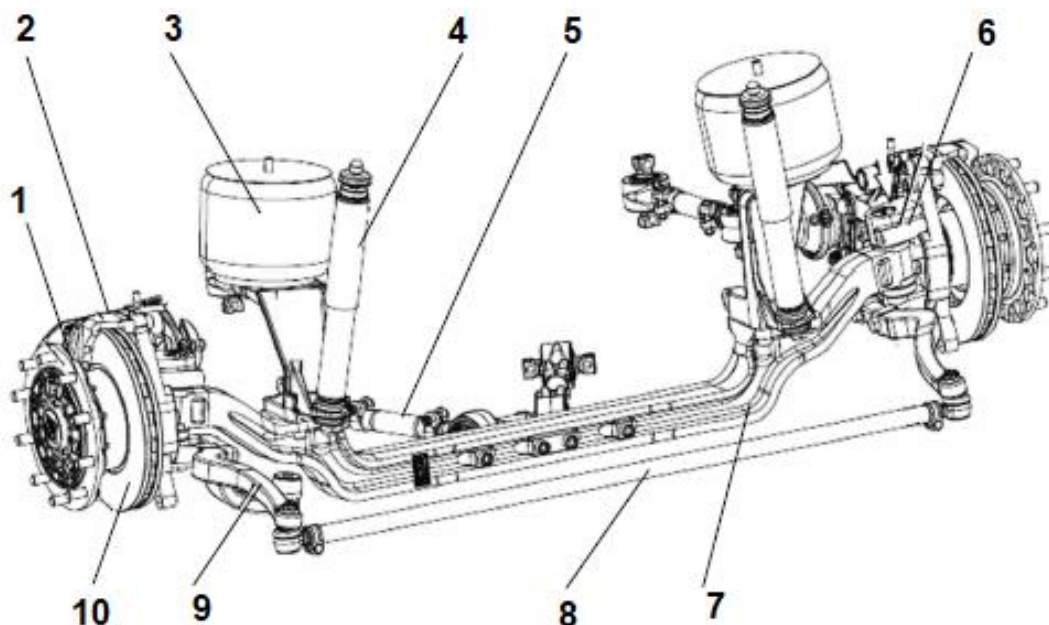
Передняя ось с реактивными штангами и пневмобаллонами подвески
